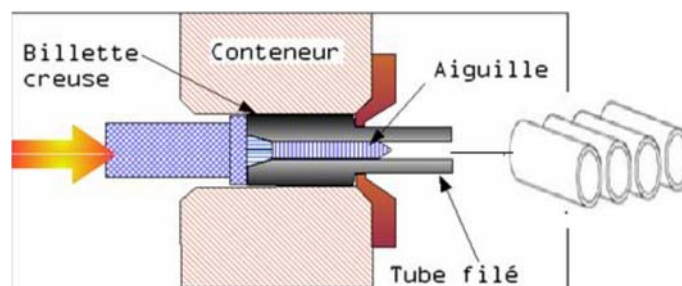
Fabrication de pipes sans soudure « schéma du filage sur aiguille permettant d'obtenir un tube sans soudure »
